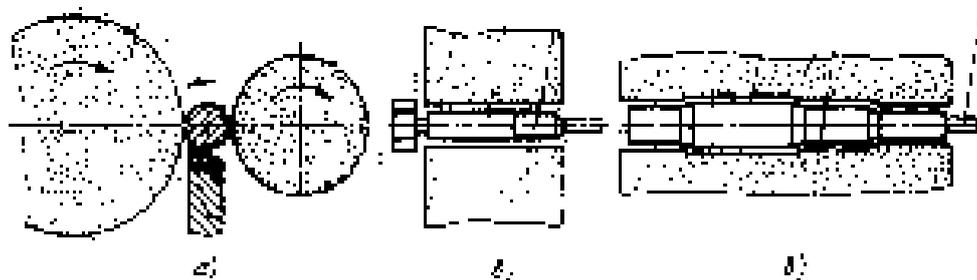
Схемы обработки на бесцентрово-шлифовальном станке
